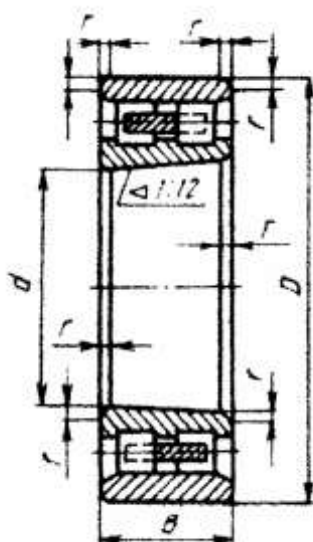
Роликовые радиальные двухрядные подшипники с короткими цилиндрическими роликами
